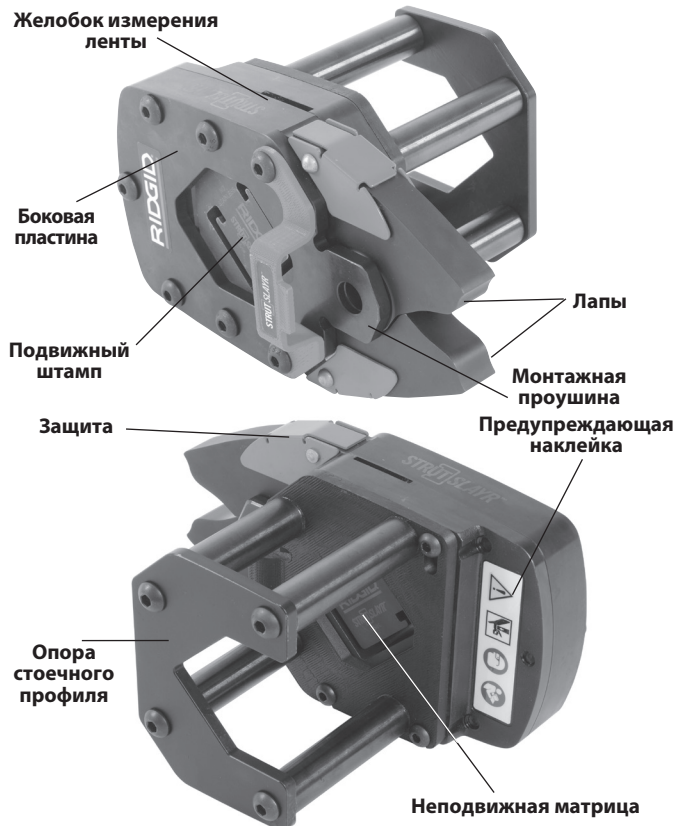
Режущая головка для стоечных профилей STRUTSLAYR
